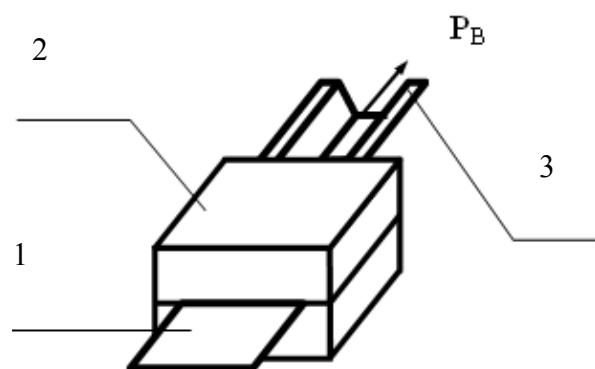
Формообразование профиля при протягивании заготовки через инструментальную фильеру:
